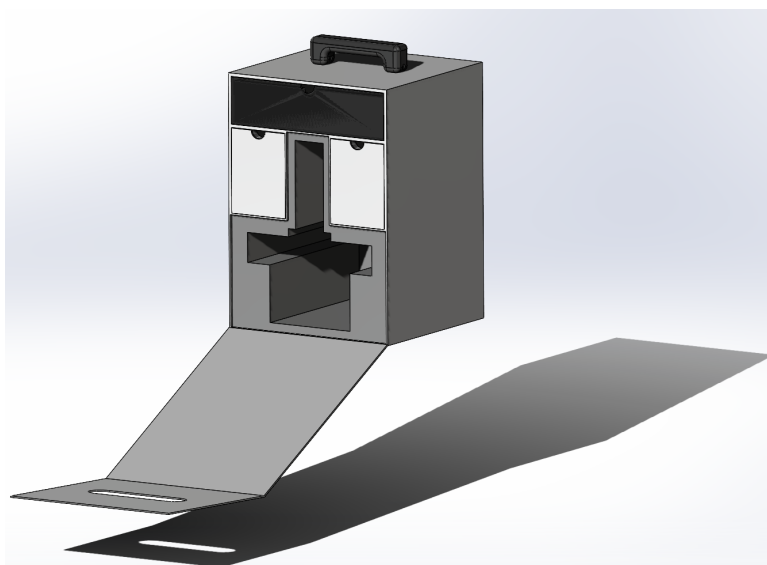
Общий вид упаковки манипулятора Hobots D
